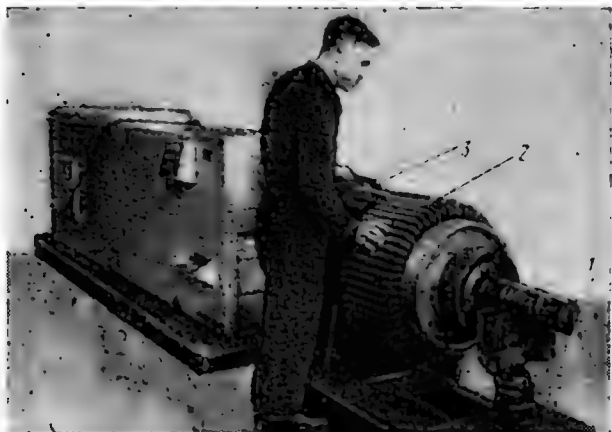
Калибровка пазов в стали якоря на протяжном станке:
